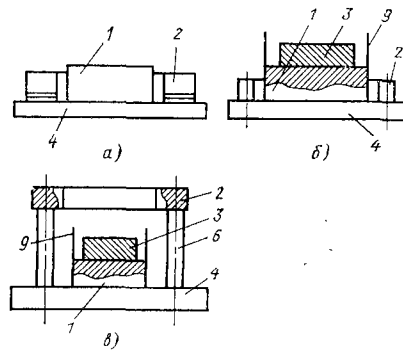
Последовательность подготовки станка для электроэрозионной обработки крупногабаритных деталей:
